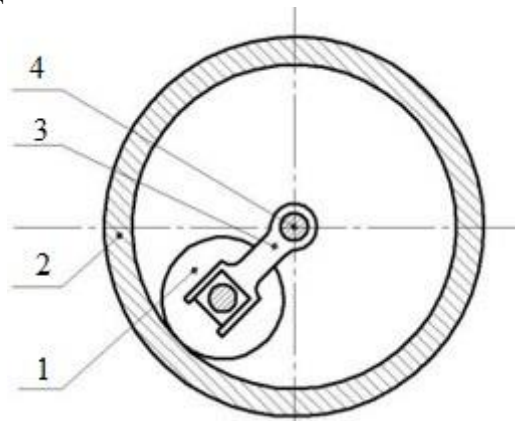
Конструкція повідково-планетарного віброзбудника коливань
